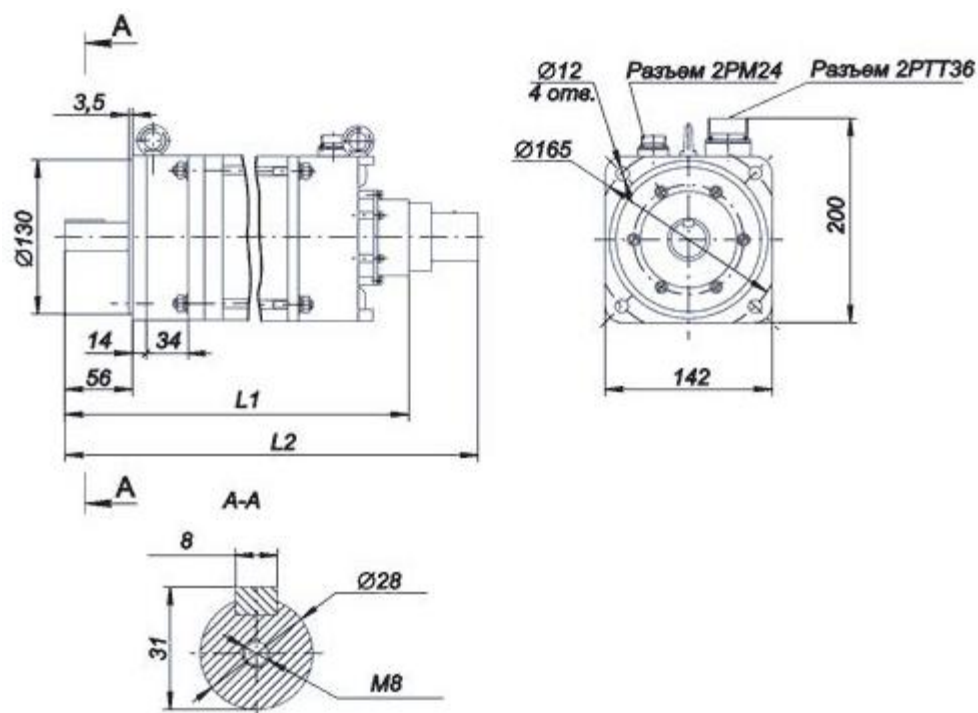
Чертеж общего вида двигателя 5ДВМ215А15
